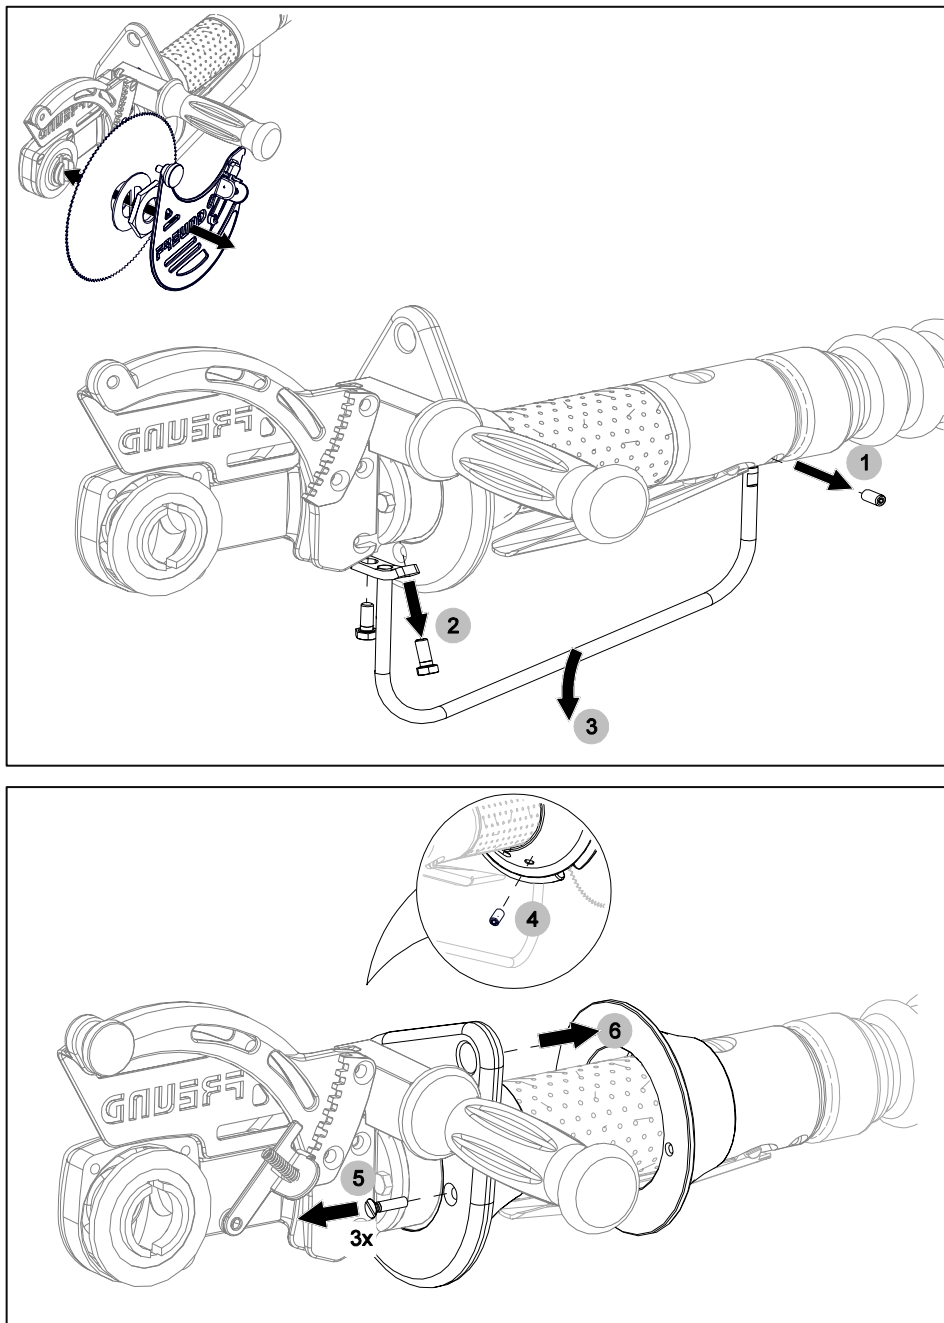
Замена смазки в редукторе с конической передачей K16-P4_evo2
